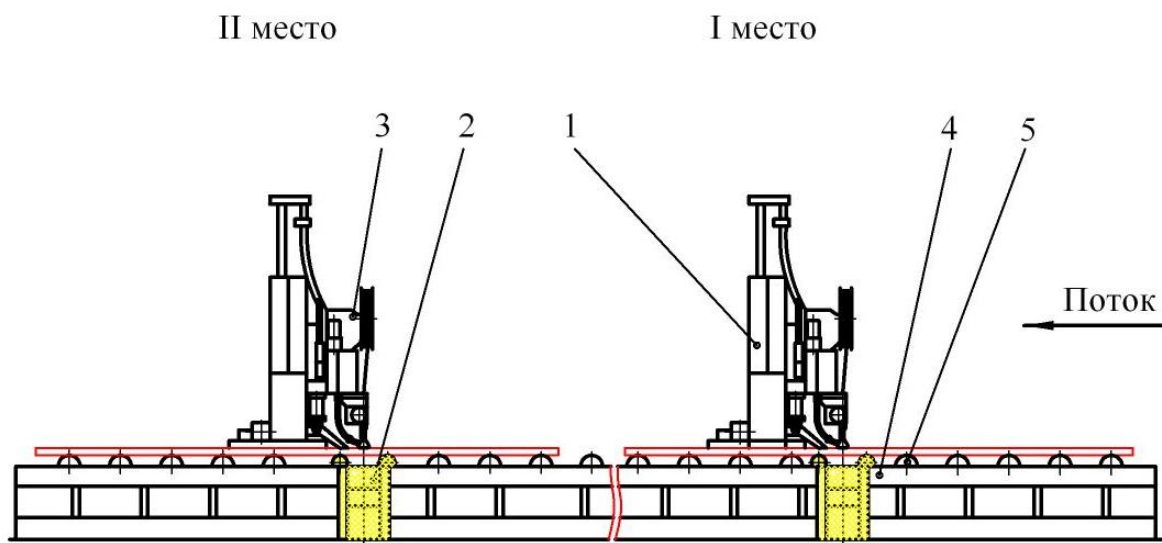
Универсальный двухместный стэнд автоматической сварки первой стороны листовых полотнищ:
